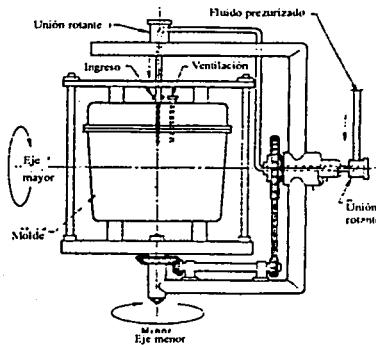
Molde de rotomoldeo montado en el brazo giratorio de la máquina.
